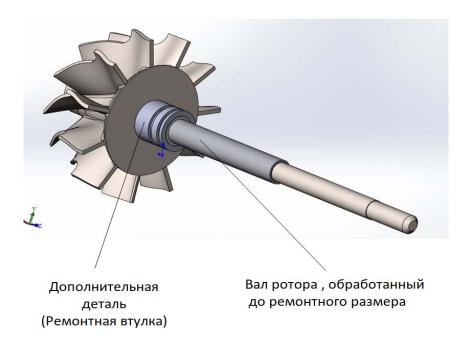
Твердотельная модель вала ротора турбокомпрессора с установленной дополнительной деталью
